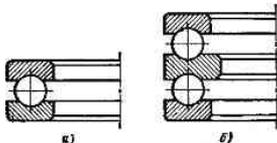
Шарикоподшипники упорные: а — одинарные; б — двойные
